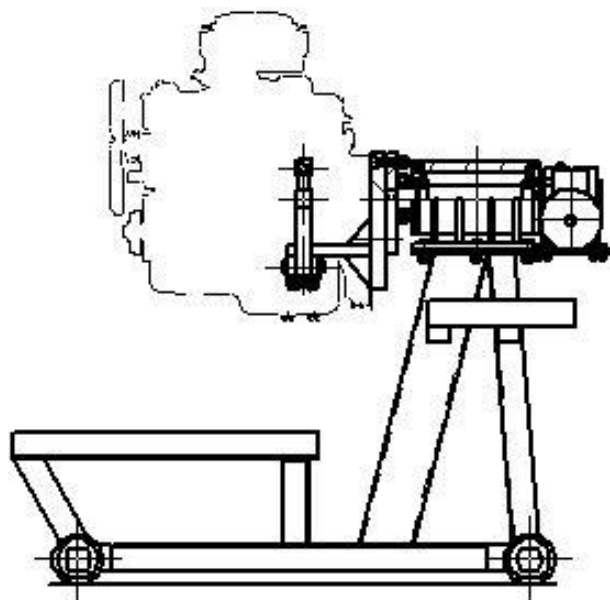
Схема устройства для разборки и сборки двигателей.
